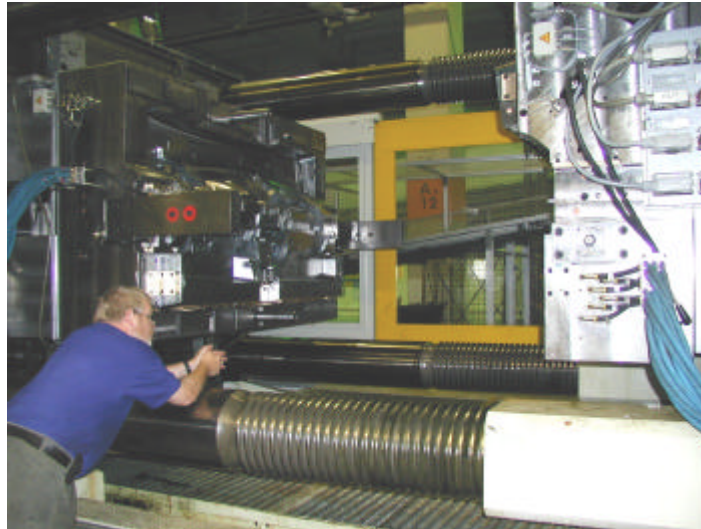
Großwerkzeug in geöffneter Stellung in der Spritzgießmaschine
